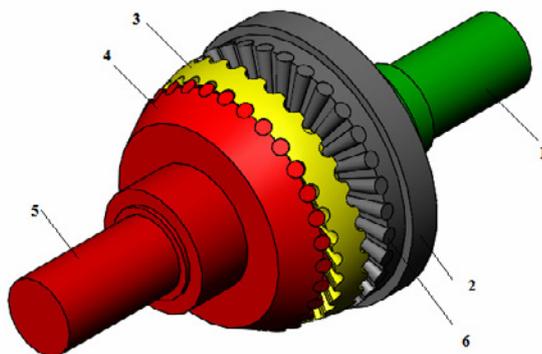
Схема кинематического редуктора с торцевыми зубьями: 1 – входный вал; 2 – входное колесо; 3 – шестерня; 4 – выходное колесо; 5 – выходный вал; 6 – зуб колеса в форме багажника конуса
